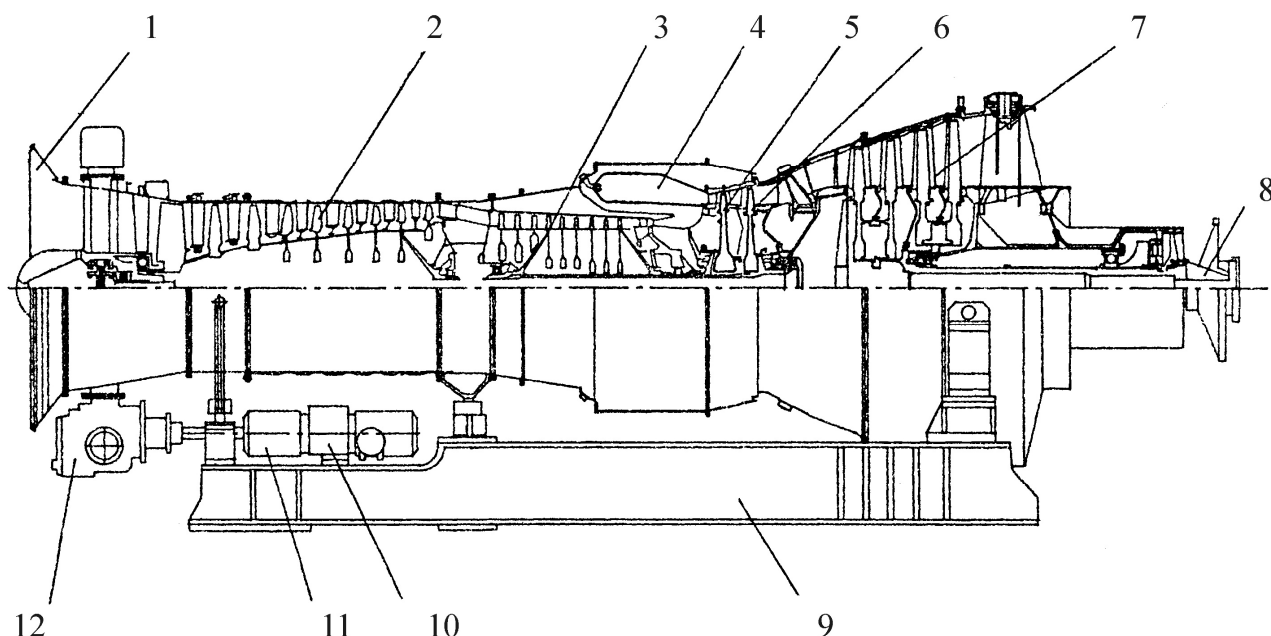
Конструктивна схема двигуна UGT 25000:
